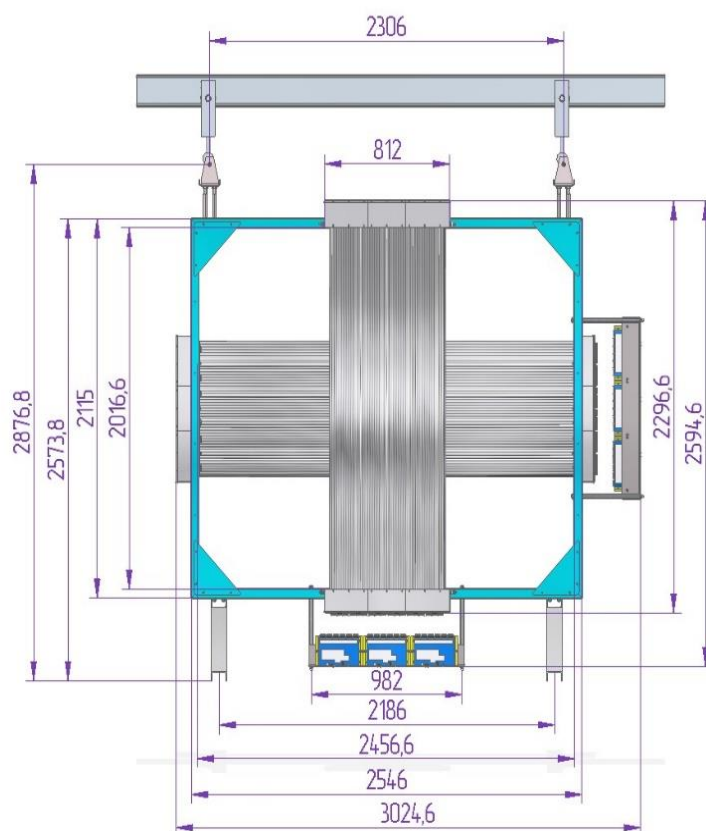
Схема дрейфовой камеры для установки ВЕС
